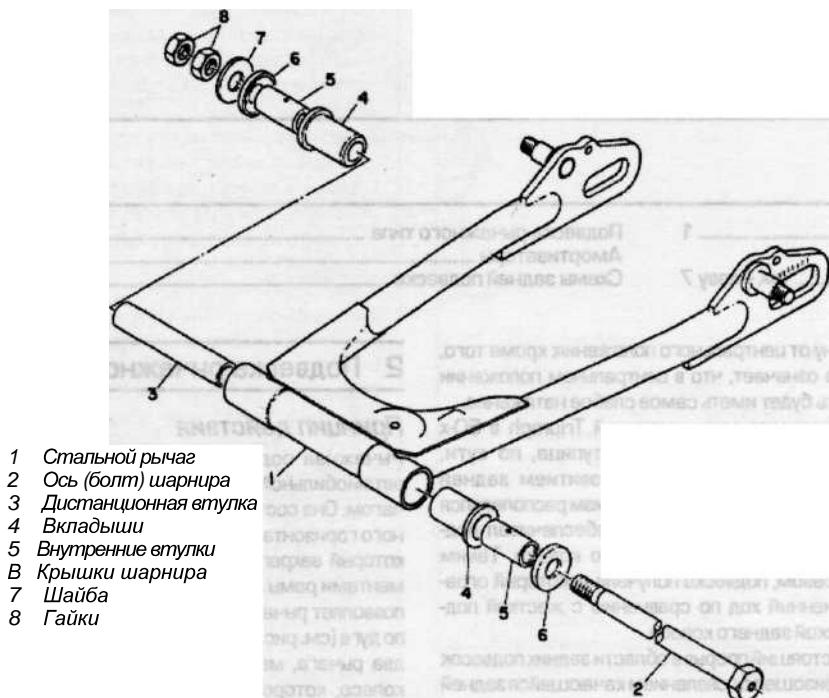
Типичный стальной рычаг подвески трубчатой конструкции
